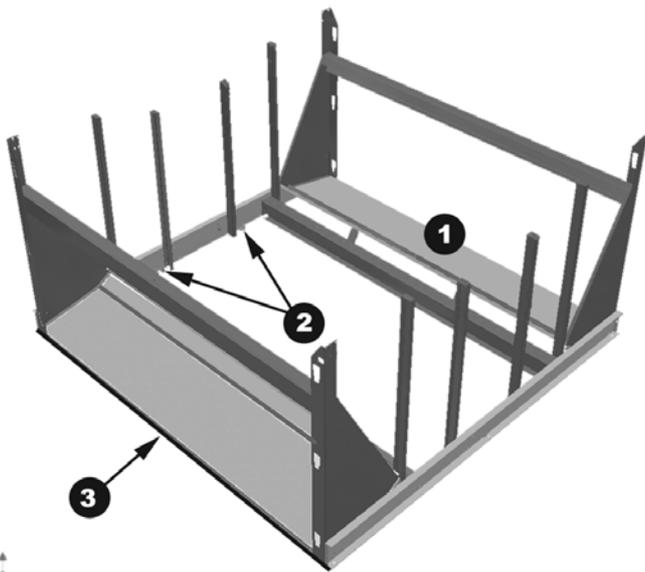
Section plenum partiellement assemblée (expédiée complètement assemblée)
